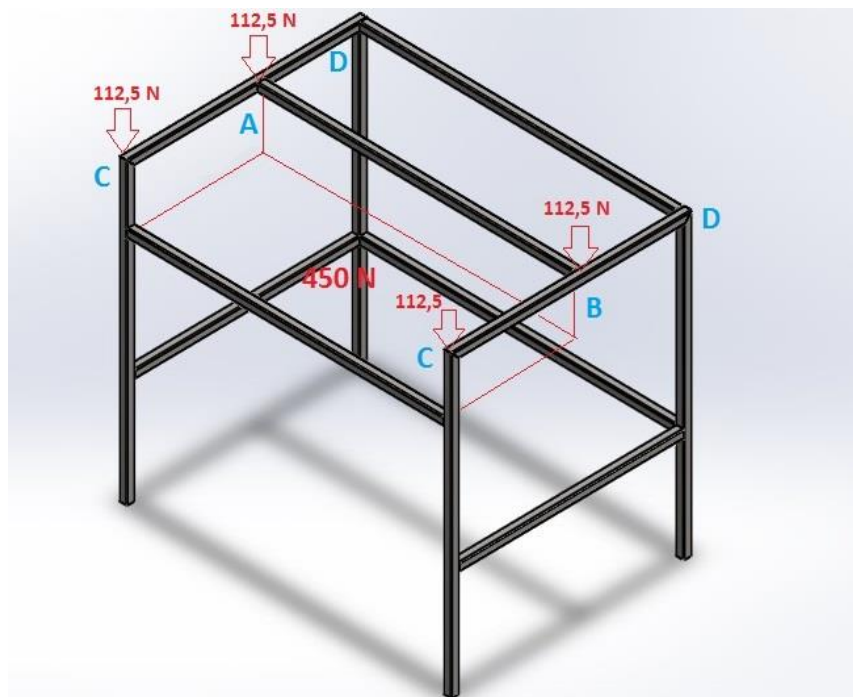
Distribución de la carga 2 en las vigas D-C
